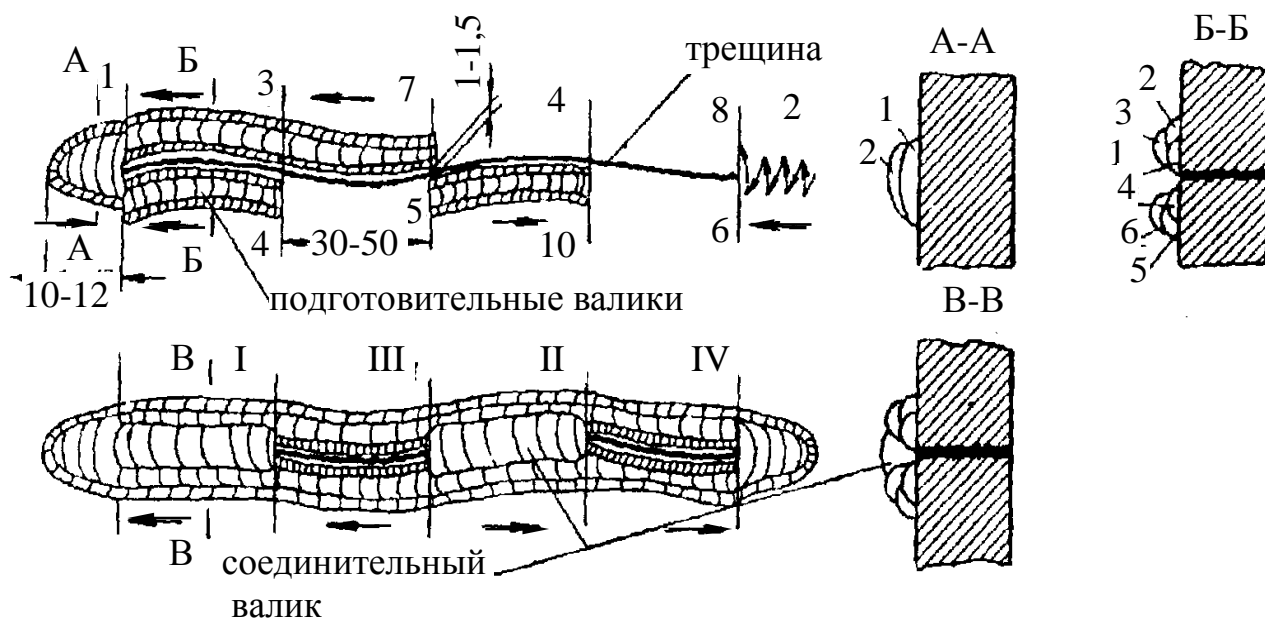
Последовательность наложения сварных валиков при заварке трещины без предварительной разделки её в тонкой стенке детали методом отжигающих валиков: I, II, III и IV – участки сварки; 1 – 10 – последовательность наложения сварных швов
